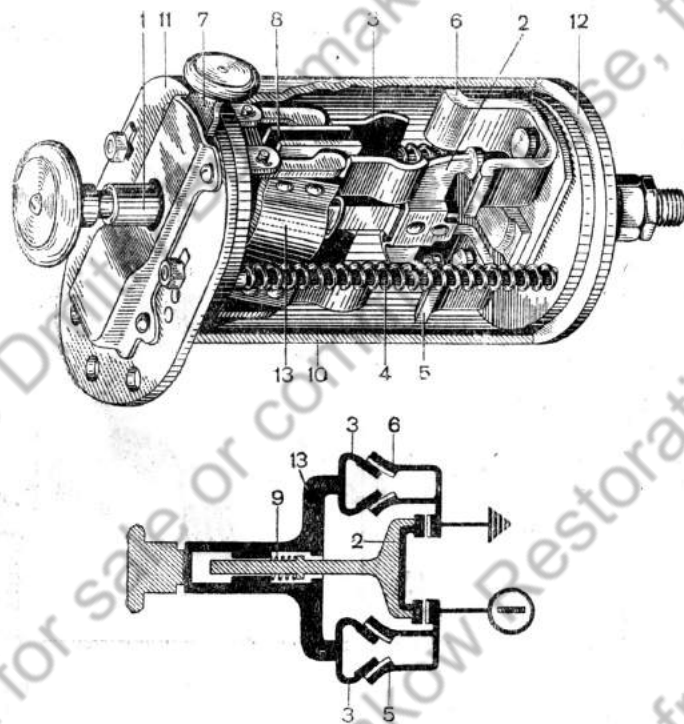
Выключатель «массы» ВВ-404 (общий вид).
